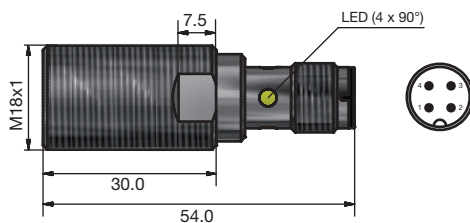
Kurze Ausführung, bündiger Einbau, Steckversion
